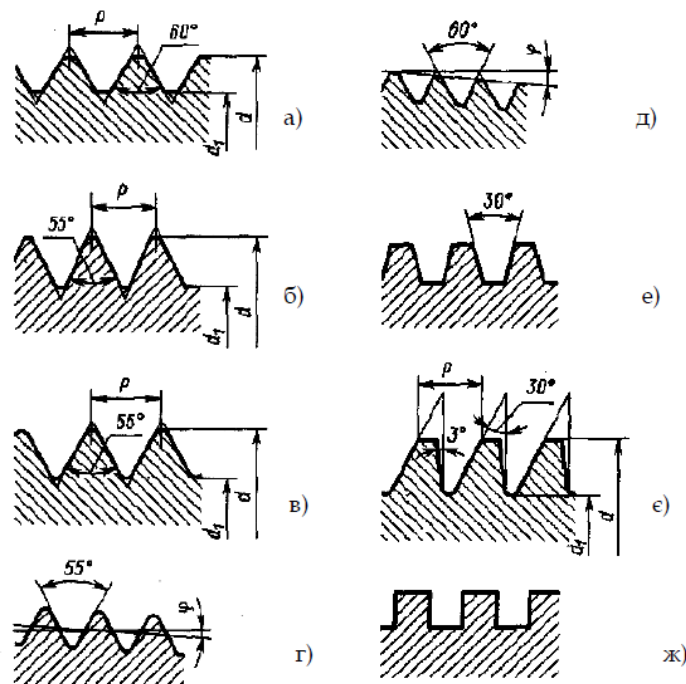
Різьба а – метрична; б – дюймова; в – трубна циліндрична; г –
